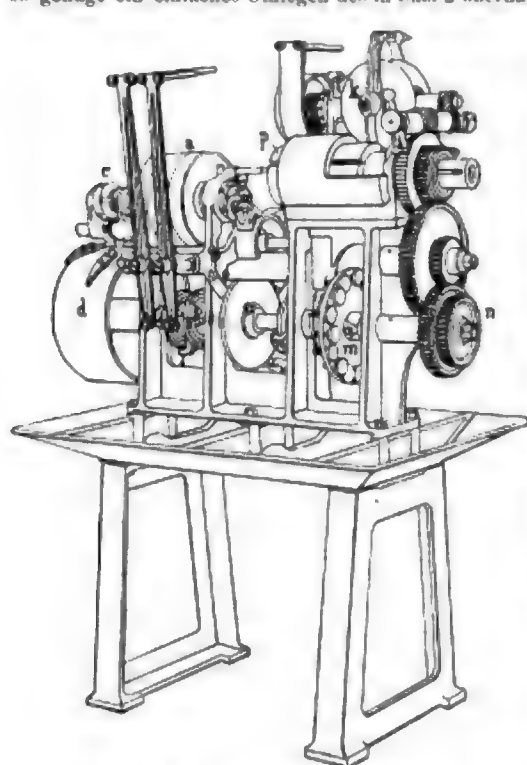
Z. A. Schrauben-Schneidmaschine.
